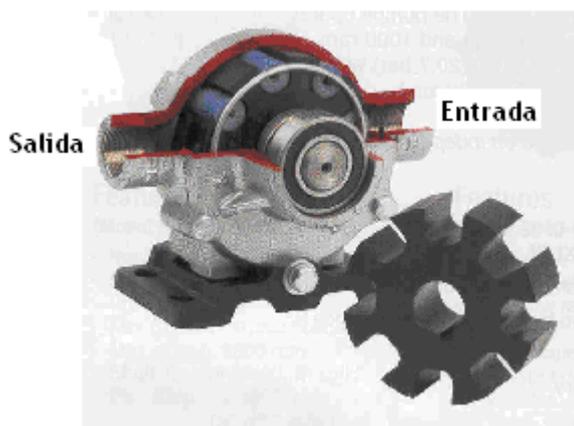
Corte de una bomba de rodillos. Fuente Hypro
